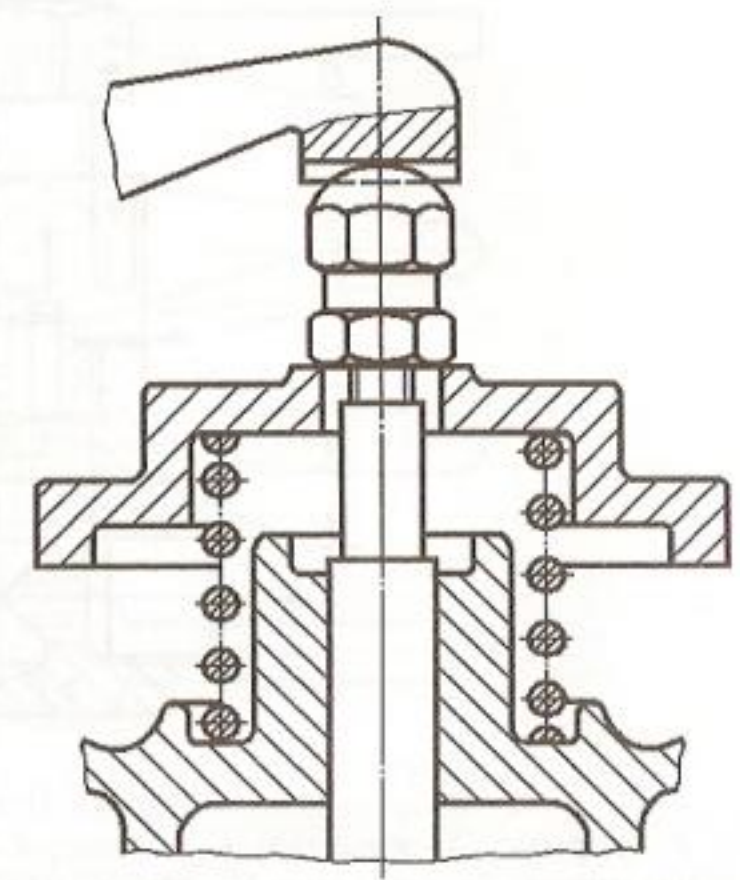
Допускаемое изображение пружины на сборочном чертеже (фрагмент вентиля)
